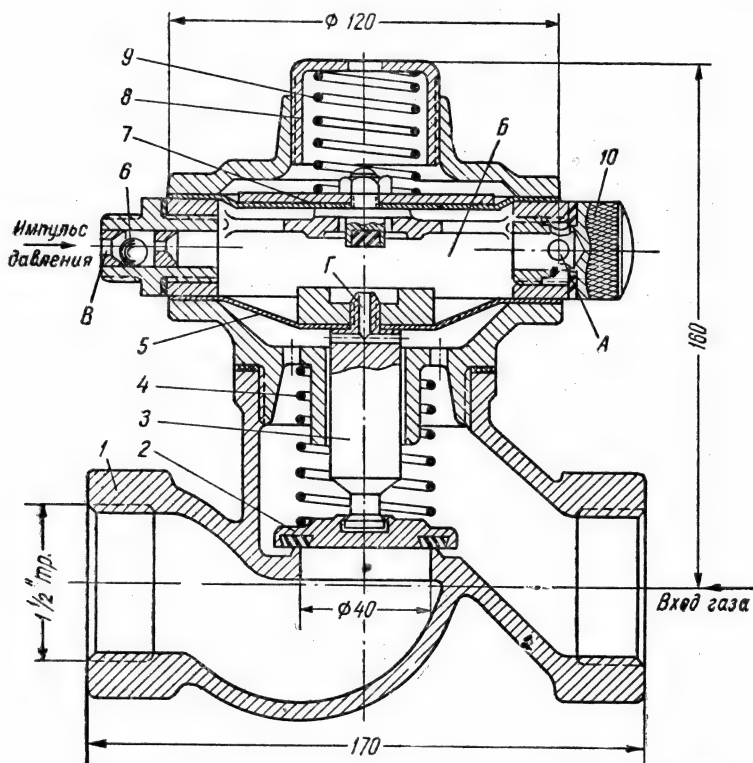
Предохранительный запорный клапан типа ПКК-40.
